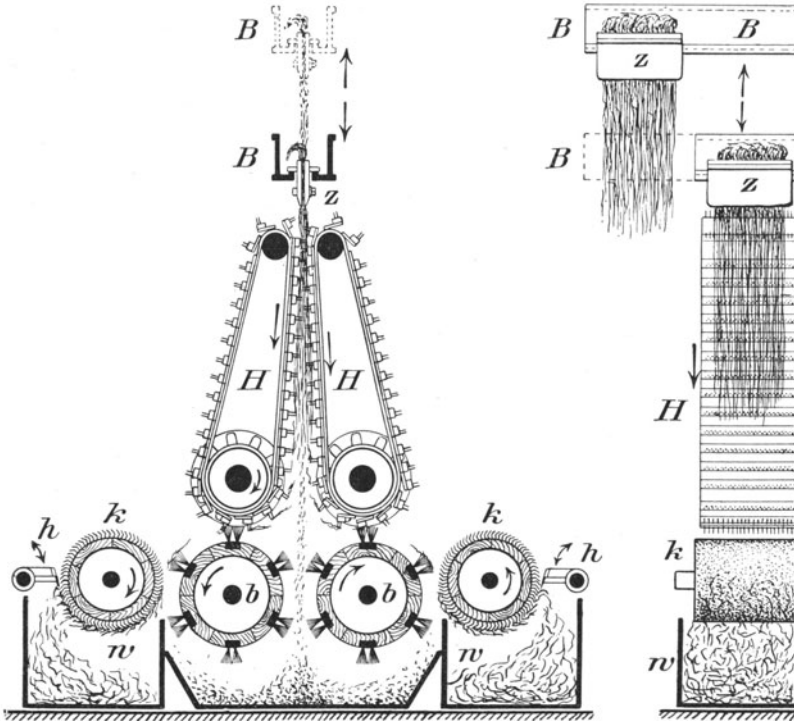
u. 123. Arbeitswerkzeuge der Hechelmaschine.
